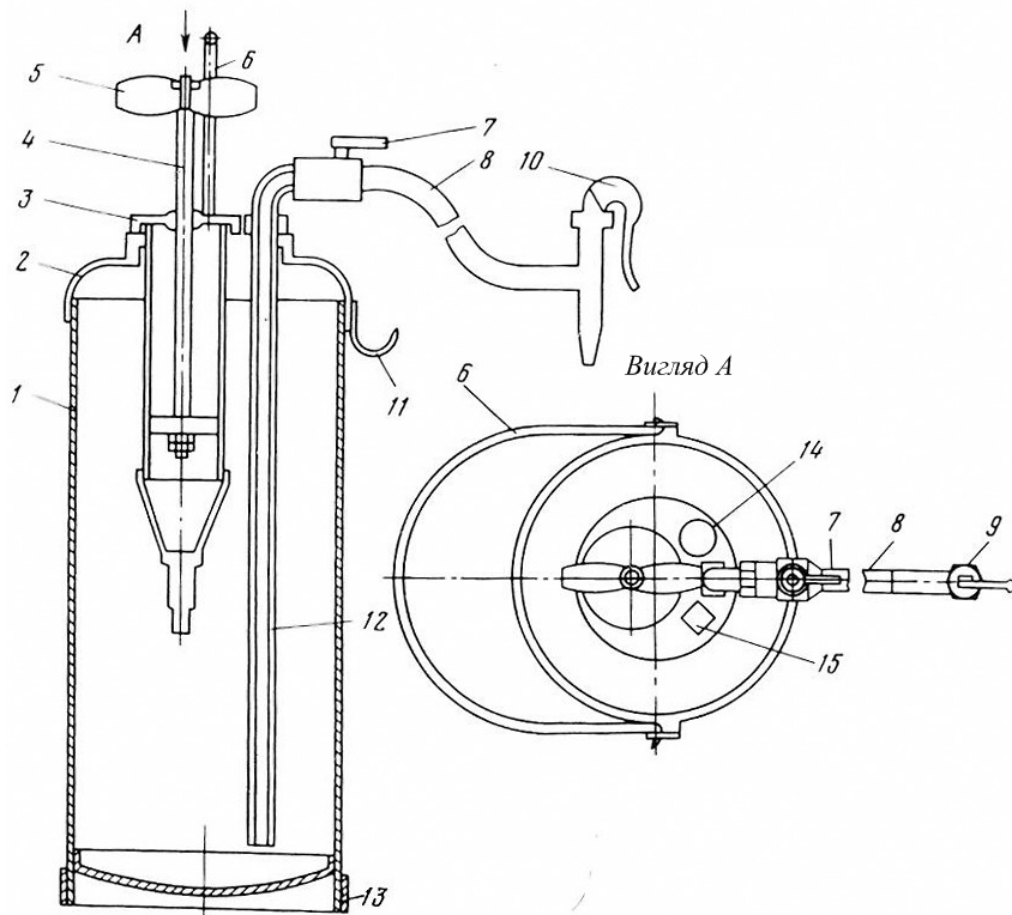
Пневматичний бачок: 1 – циліндр; 2 – днище верхнє; 3 – повітряний насос; 4 – шток; 5 – рукоятка; 6 – ручка; 7 – кран; 8 – гумовий рукав; 9 – наконечник з кульовим клапаном; 10 – ричаг; 11 – гачок; 12 – трубка; 13 – обичайка; 14 – випускний отвір; 15 – заливний пристрій
